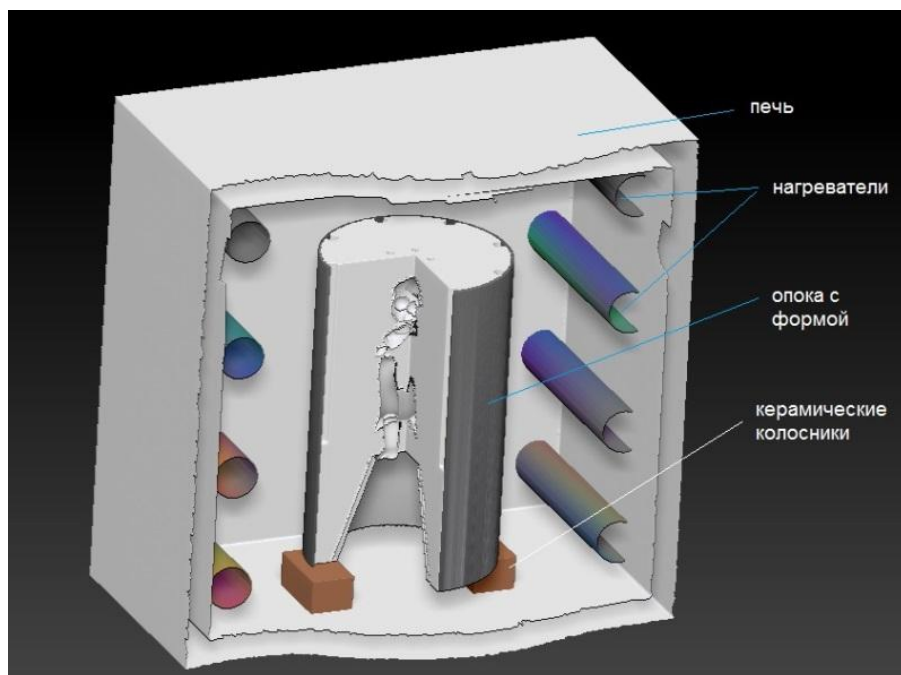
Схема установки опоки с формой в печь для сушки и обжига
